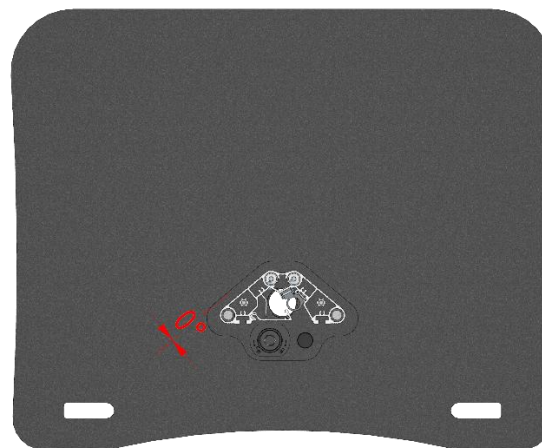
Richtige Positionierung im verriegelten Zustand
